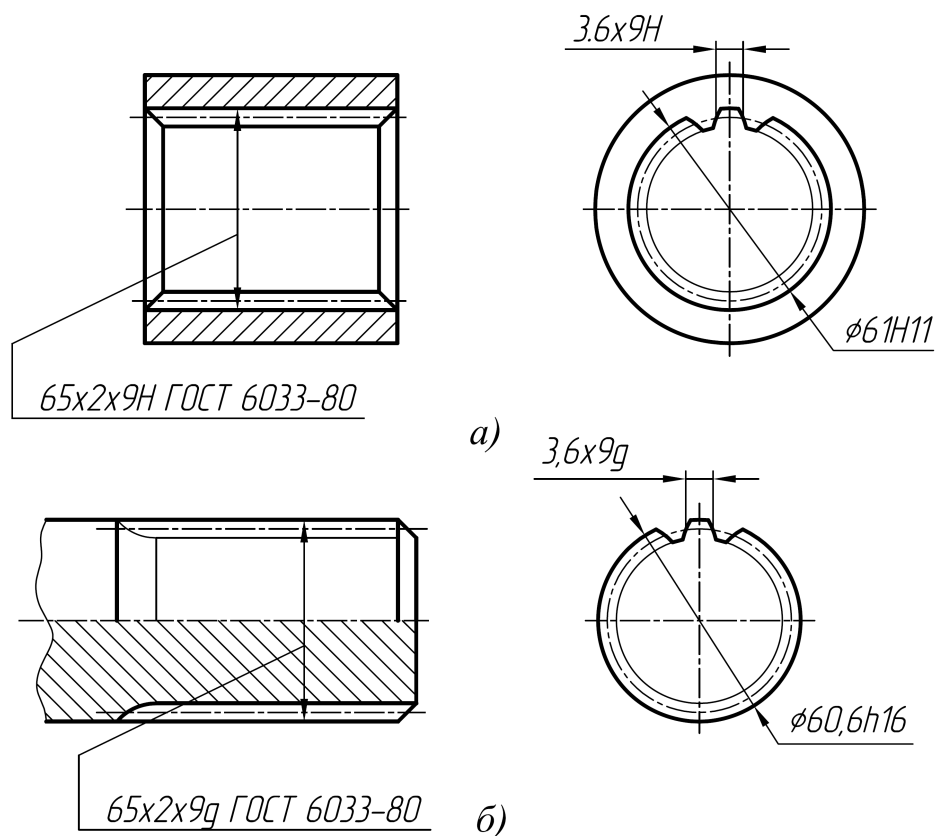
Ескізи: а) шліцьової втулки; б) шліцьового вала
